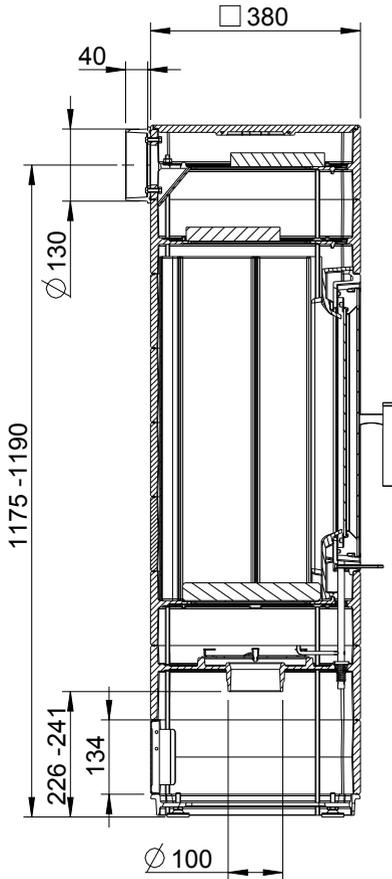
Sortie des fumées, dimensions pour une buse raccordée vers l'arrière- CORNA, CORNA tec ou CORNA ES
